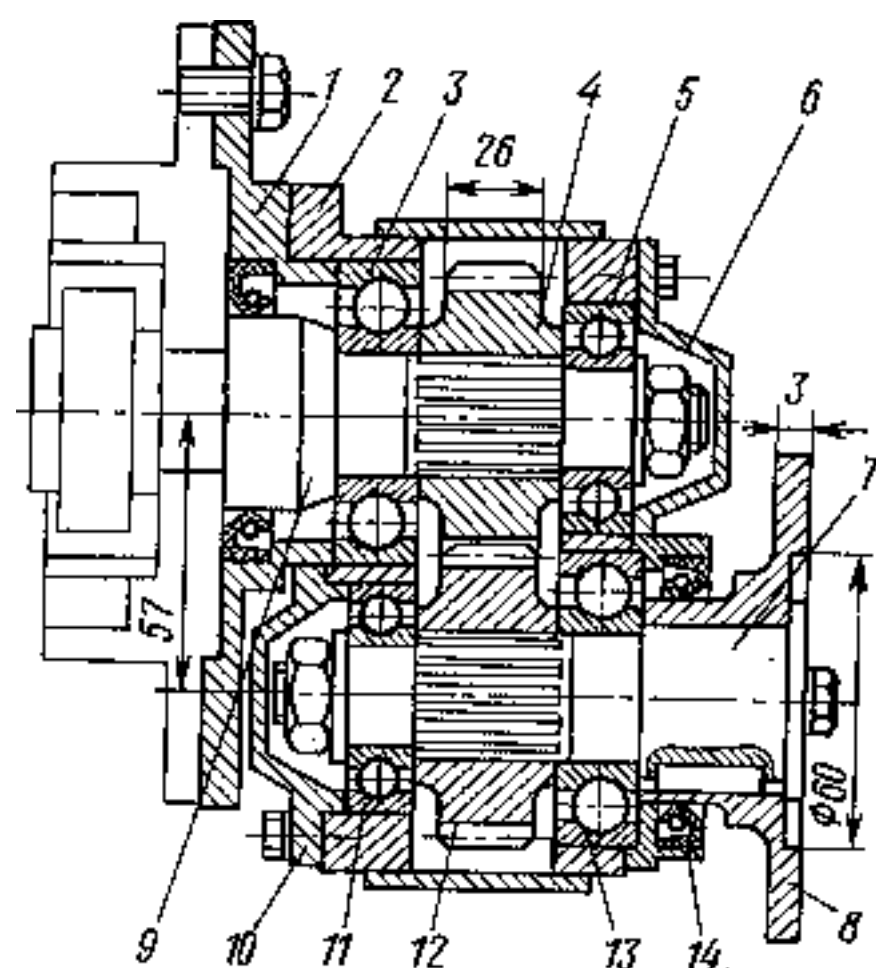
Колесный редуктор автомобиля «Нейва»:
